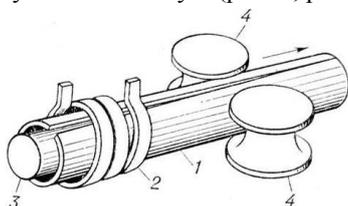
Схема высокочастотной сварки труб индукционным способом: 1 — труба; 2 — индуктор; 3 — сердечник; 4 — обжимные ролики.
